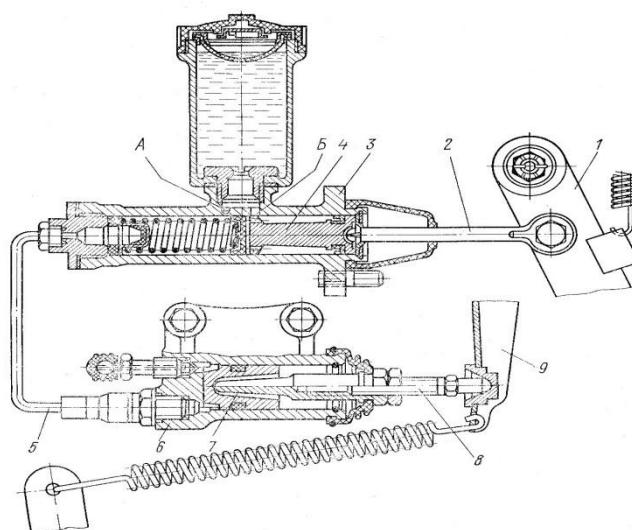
Гидравлический привод выключения сцепления: 1 – педаль управления сцеплением; 2 – толкатель; 3 – главный цилиндр; 4 – поршень; 5 – трубопровод; 6 – рабочий цилиндр; 7 – поршень; 8 – толкатель; 9 – вилка
